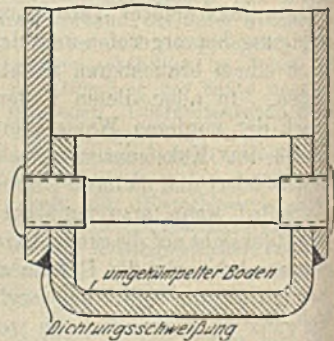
Eingehängter Boden mit Dichtungsschweißung.
